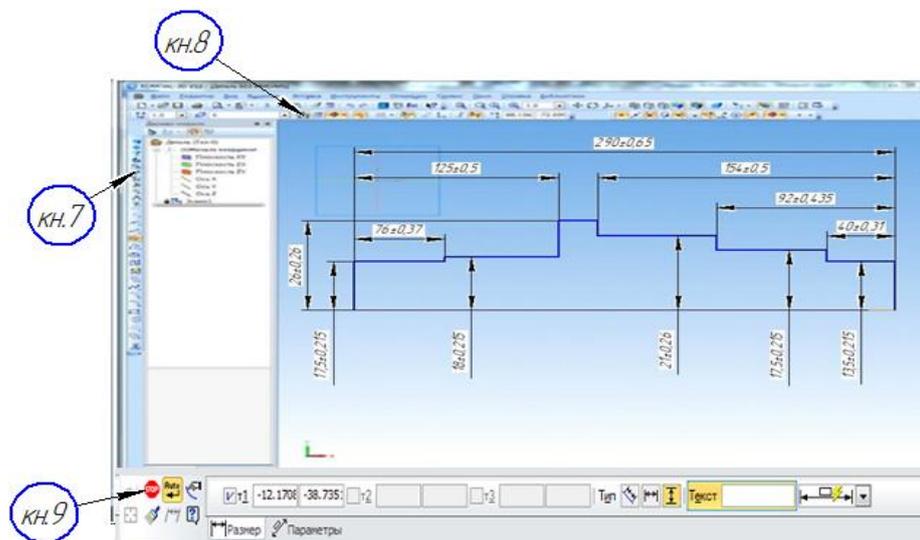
Изображение эскиза и обозначение размеров детали
